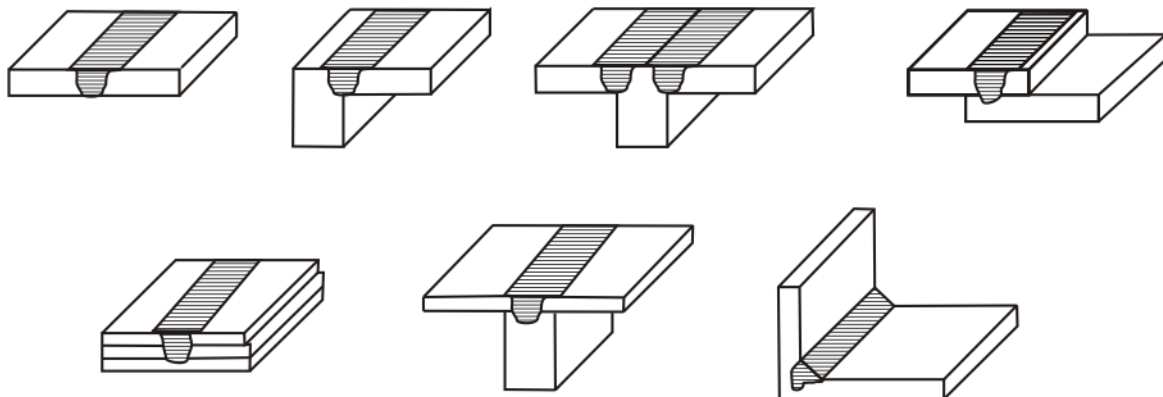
Durch Rührreißschweißen herstellbare Stoßformen (nach [17])
